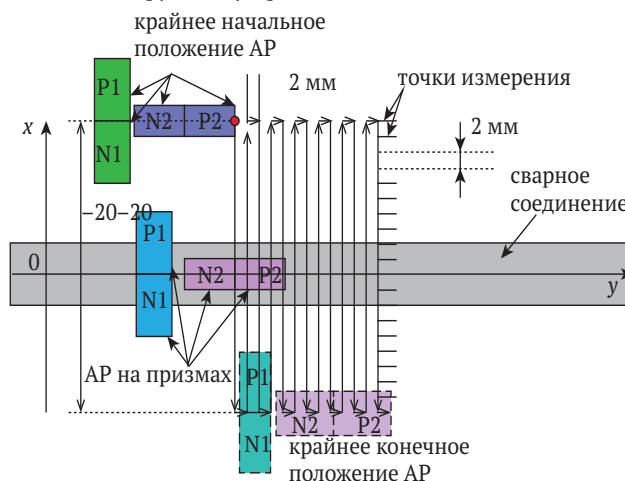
Схема сканирования сварного соединения ротора
